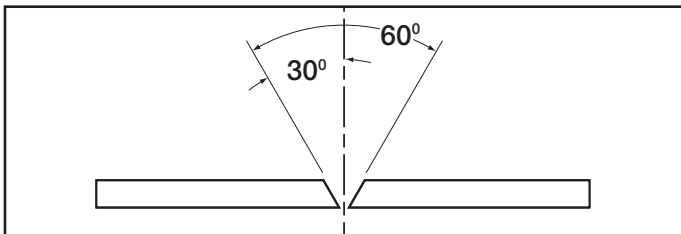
Chaflán de 30 Adecuado Para Soldadura
